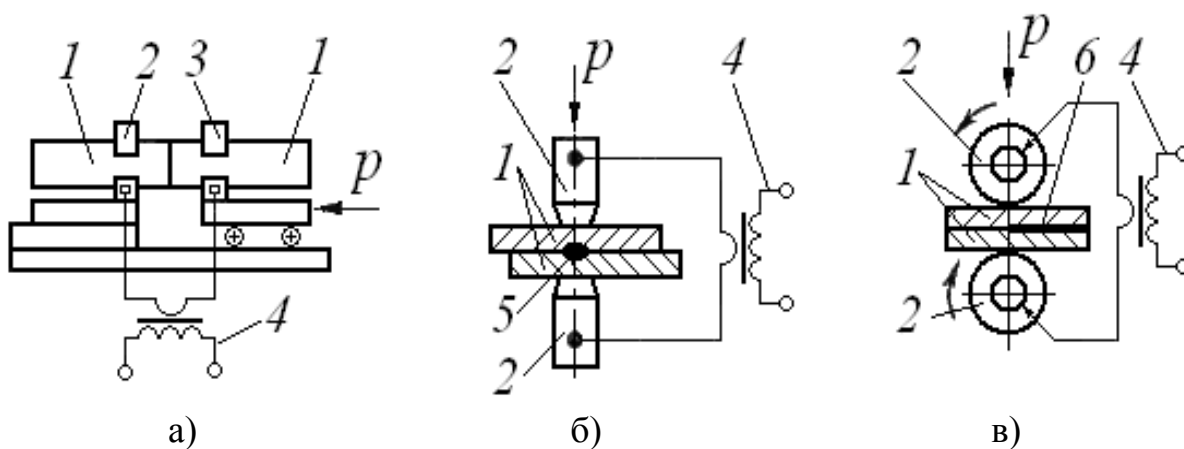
Схемы контактной сварки: стыковая (а), точечная (б) и шовная (в)
